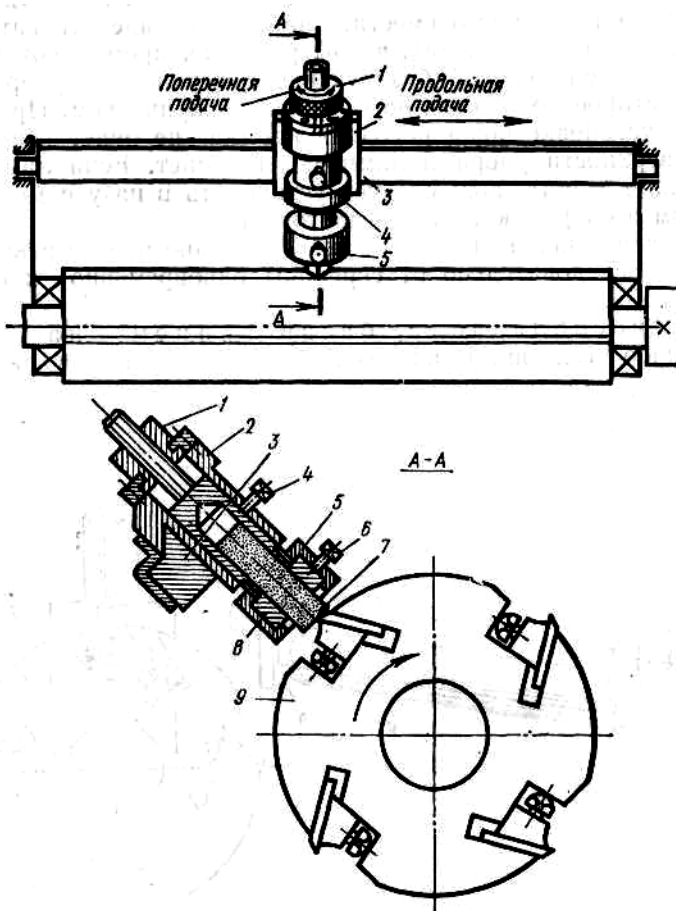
Приспособление с ручным приводом для прифуговки ножей в ножевом валу рейсмусового станка:
